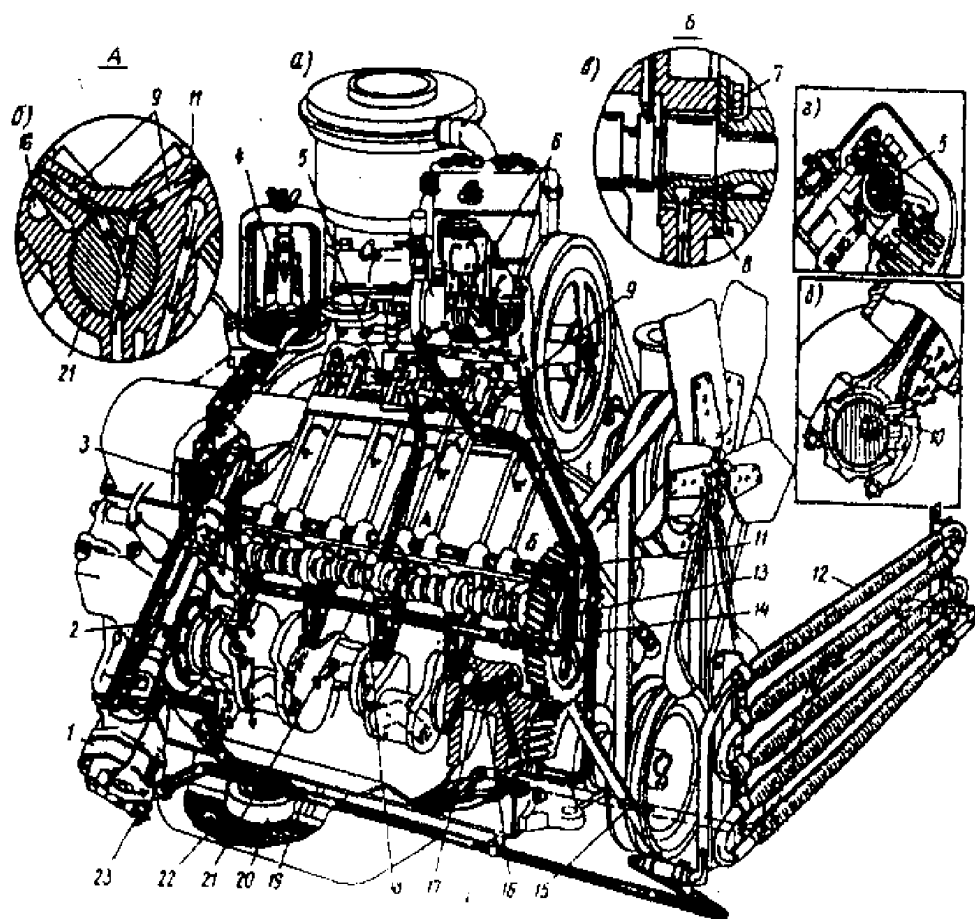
Смазочная система двигателя ЗИЛ-130: а – общая схема; б – подача масла к средней шейке распределительного вала; в – смазывание передней шейки и зубчатых колес привода распределительного вала; г – подача масла от оси коромысла к регулировочному винту и наконечнику штанги; д – смазывание стенок цилиндров.
